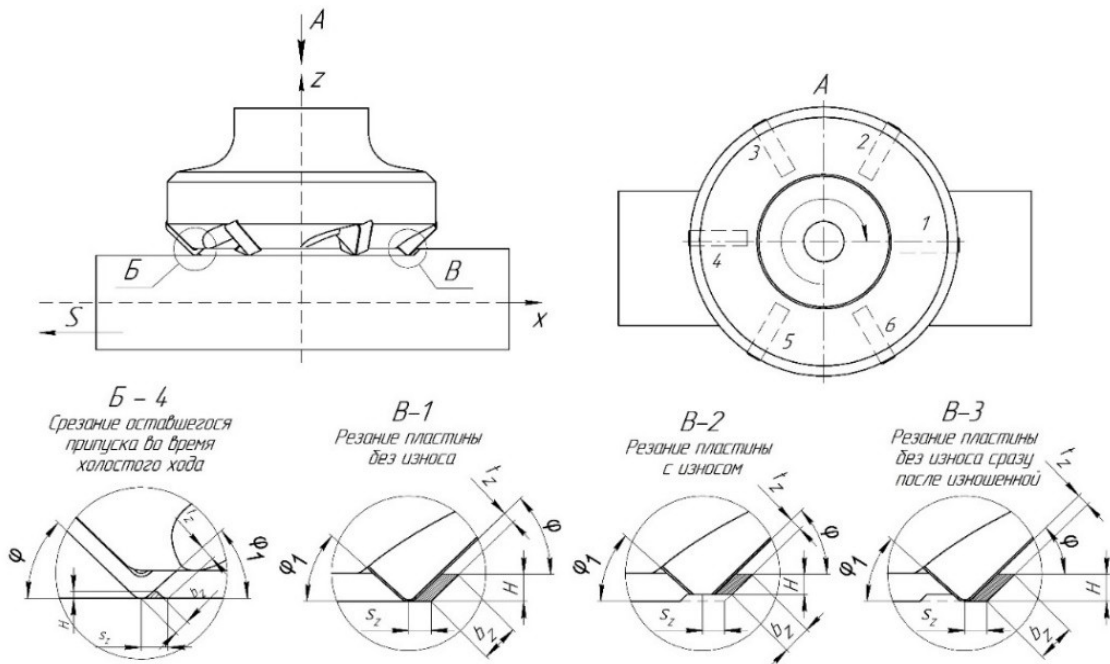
Схема процесса фрезерования чугунной поверхности при неравномерном износе режущих керамических пластин
